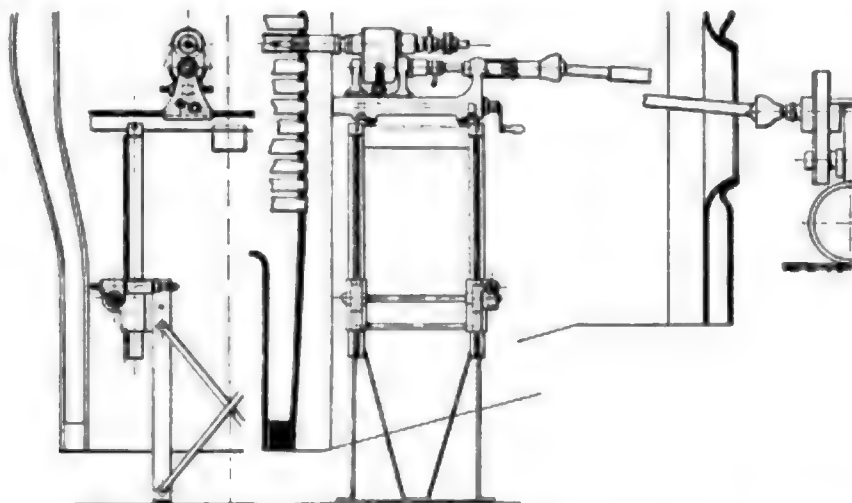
Aufwalzmaschine für Heizrohre mit elektrischem Antrieb (Werkzeugmaschinenfabrik Collet & Engelhard).
